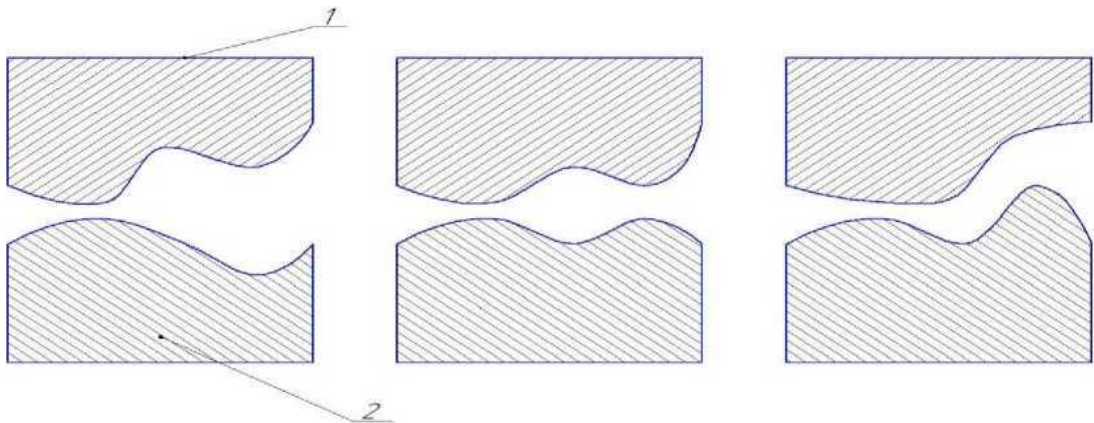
Варіанти розташування мікрорівномірностей виїмки і виступу між робочими поверхнями голки і корпусом форсунки-розпилювача: 1 - корпус; 2 - голка.
